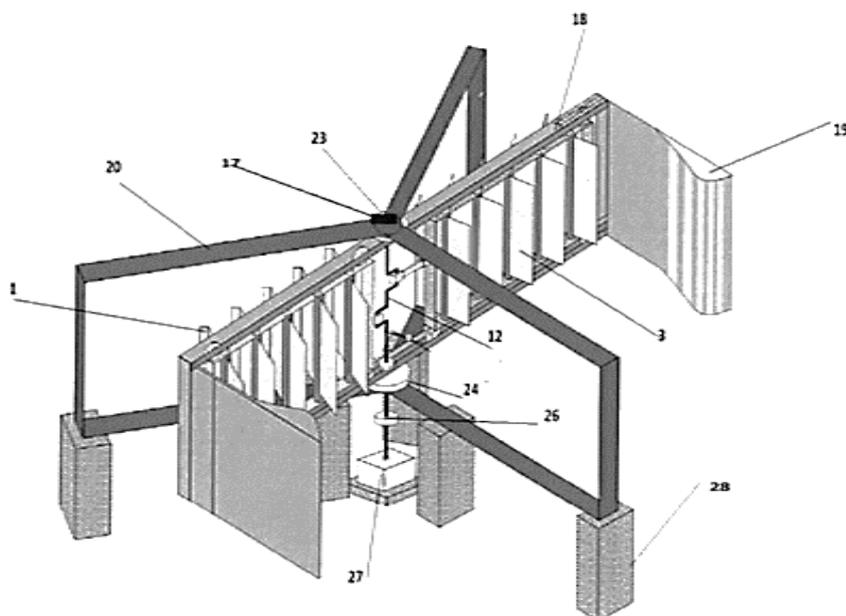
Общий вид ветродвигателя с коленчатым валом
